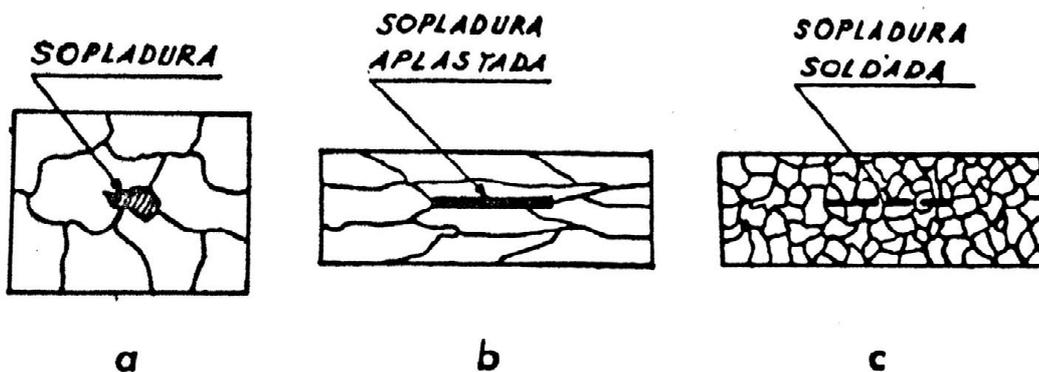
Soldadura por forja de una cavidad o sopladura; a), estado inicial; b), aplastamiento de la cavidad por la forja; c), soldadura de las dos caras por la recristalización del grano en la forja (Calvo Rodés).
